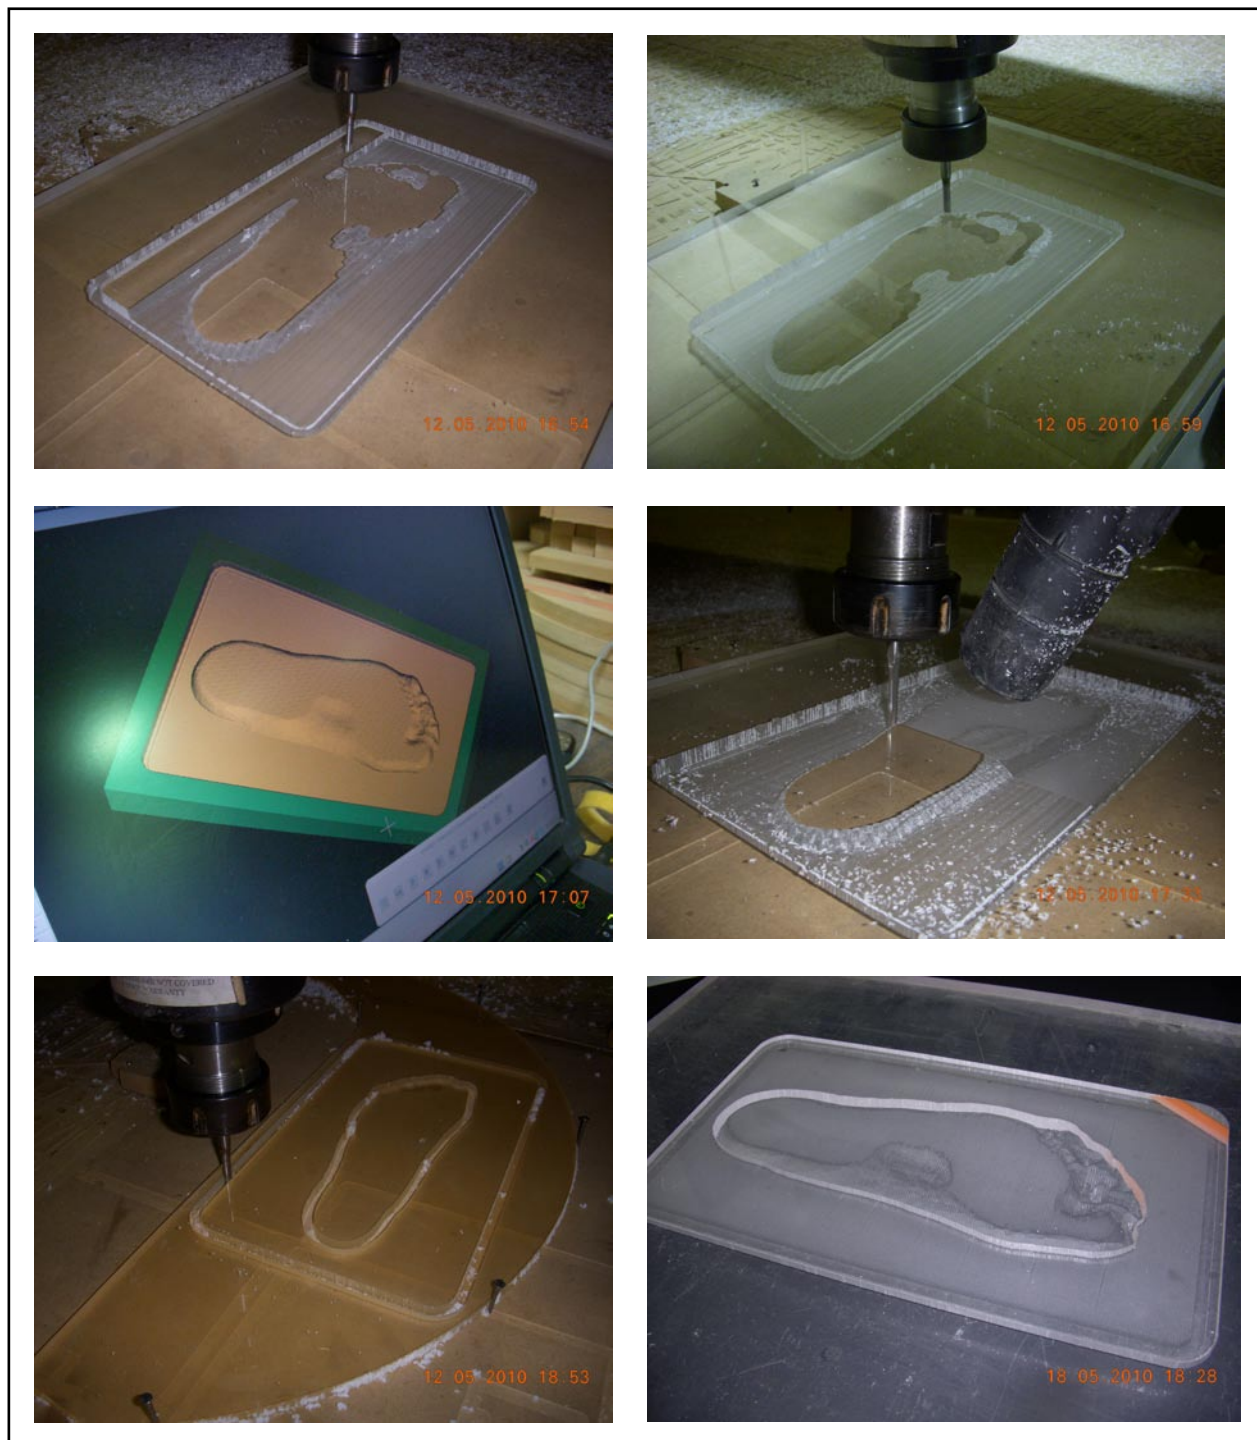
Proceso de manufactura de molde para prototipo de plantilla para pie plano
